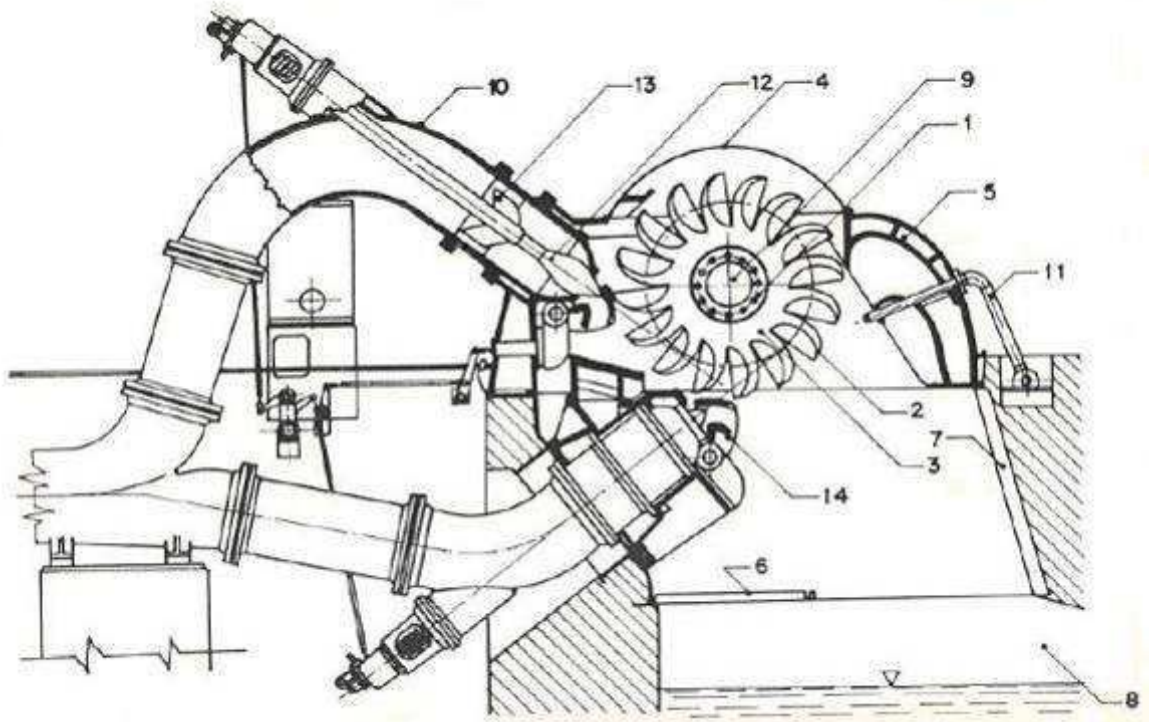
Corte transversal em uma turbina Pelton com 2 injetores, eixo horizontal, com indicação dos seus componentes principais: (1) rotor, (2) pá em forma de concha do rotor, (3) coroa das pás, (4) tampa, (5) desviador frontal, (6) poço, (7) blindagem, (8) canal de fuga, (9) eixo da turbina, (10) injetor, (11) freio do jato, (12) agulha de regularização, (13) cruzeta Pelton e (14) defletor de jato. [Fonte: Souza, 1983, p.140.]
